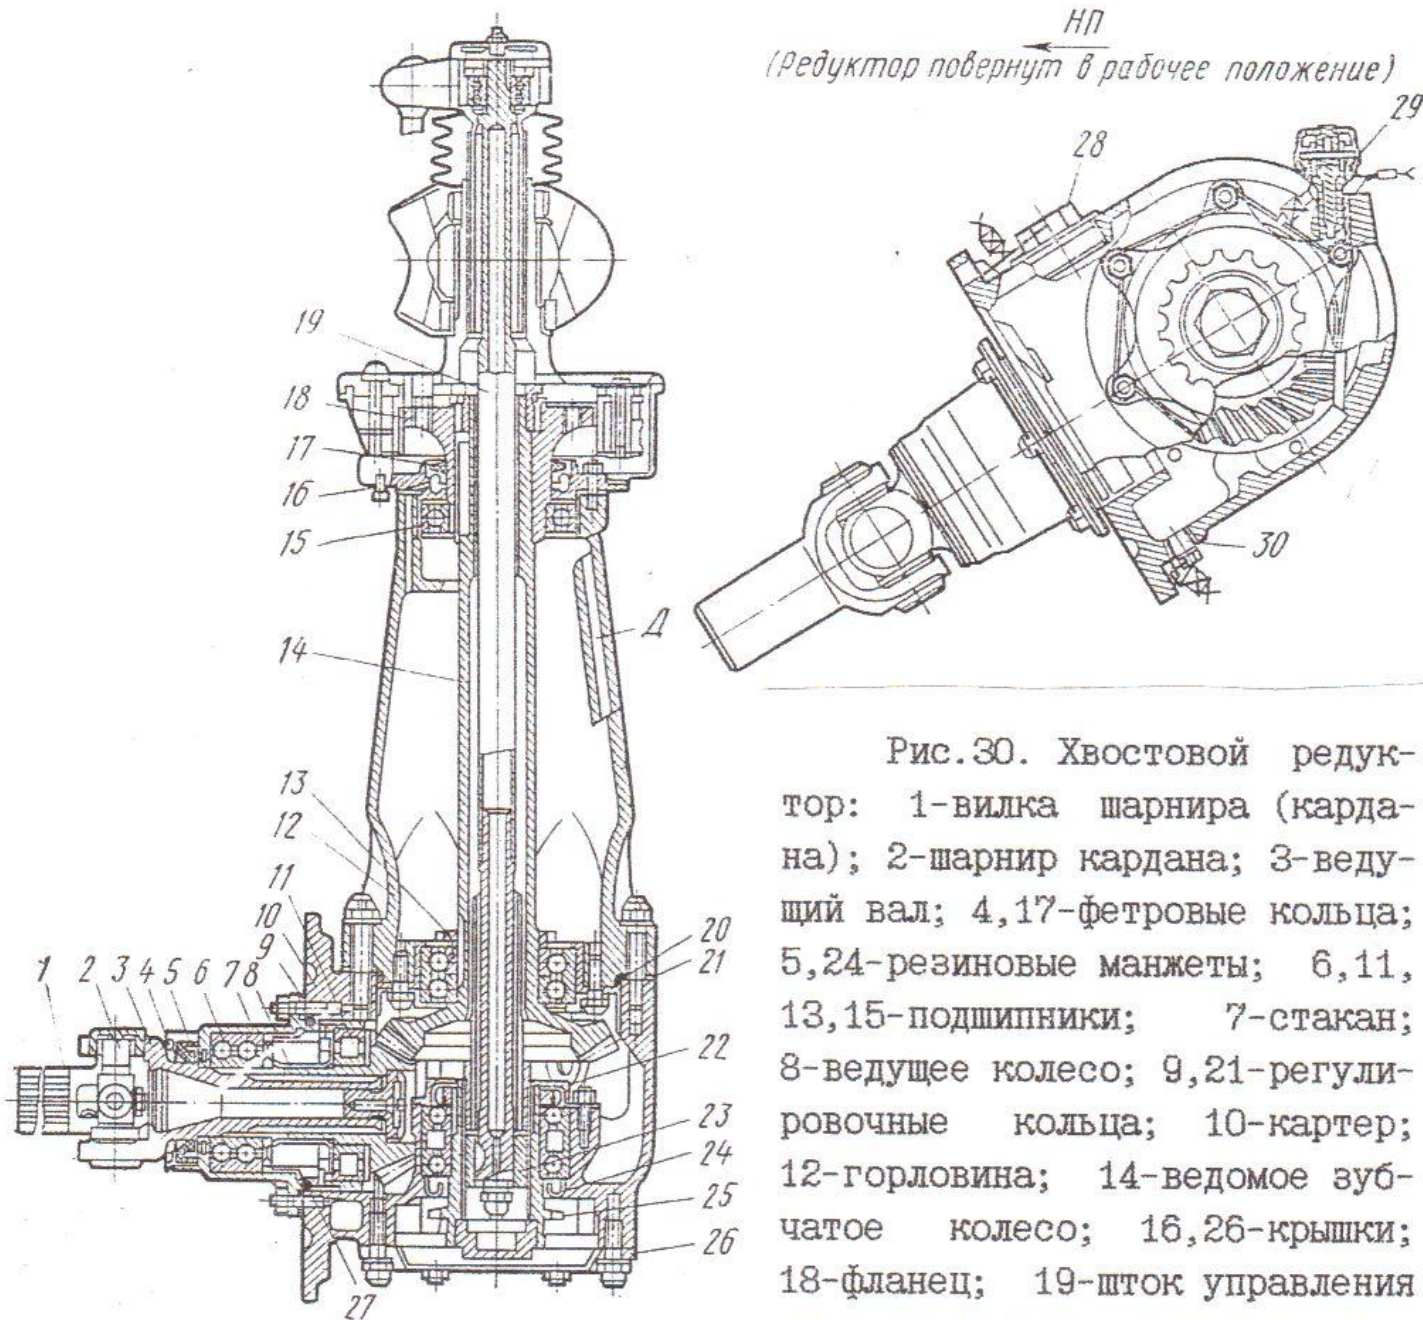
Хвостовой редуктор: 1-вилка шарнира (кардана); 2-шарнир кардана; 3-ведущий вал; 4,17-фетровые кольца; 5,24-резиновые манжеты; 6,11,13,15-подшипники; 7-стакан; 8-ведущее колесо; 9,21-регулирующие кольца; 10-картер; 12-горловина; 14-ведомое зубчатое колесо; 16,26-крышки; 18-фланец; 19-шток управления
